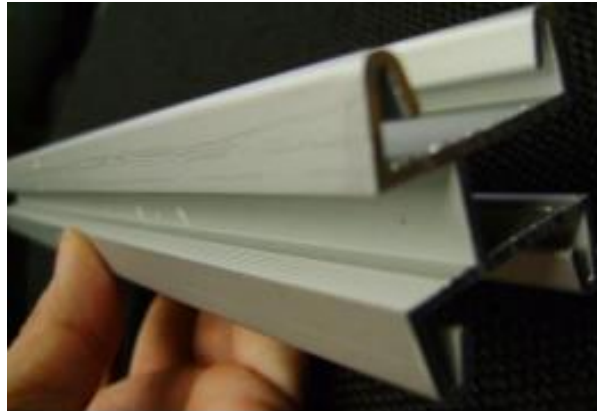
Grietas en el perfil de aluminio [25]
